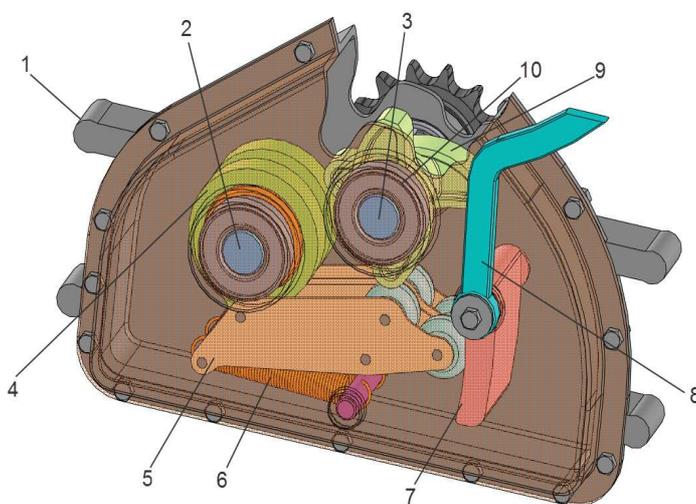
Конструкция бесступенчатого редуктора: 1 – корпус; 2 – вал ведомый; 3 – вал ведущий; 4 – обгонные муфты; 5 – рычаги толкателей; 6 – пружины; 8 – регулировочный рычаг; 9 – кулачки; 10 – подшипники
